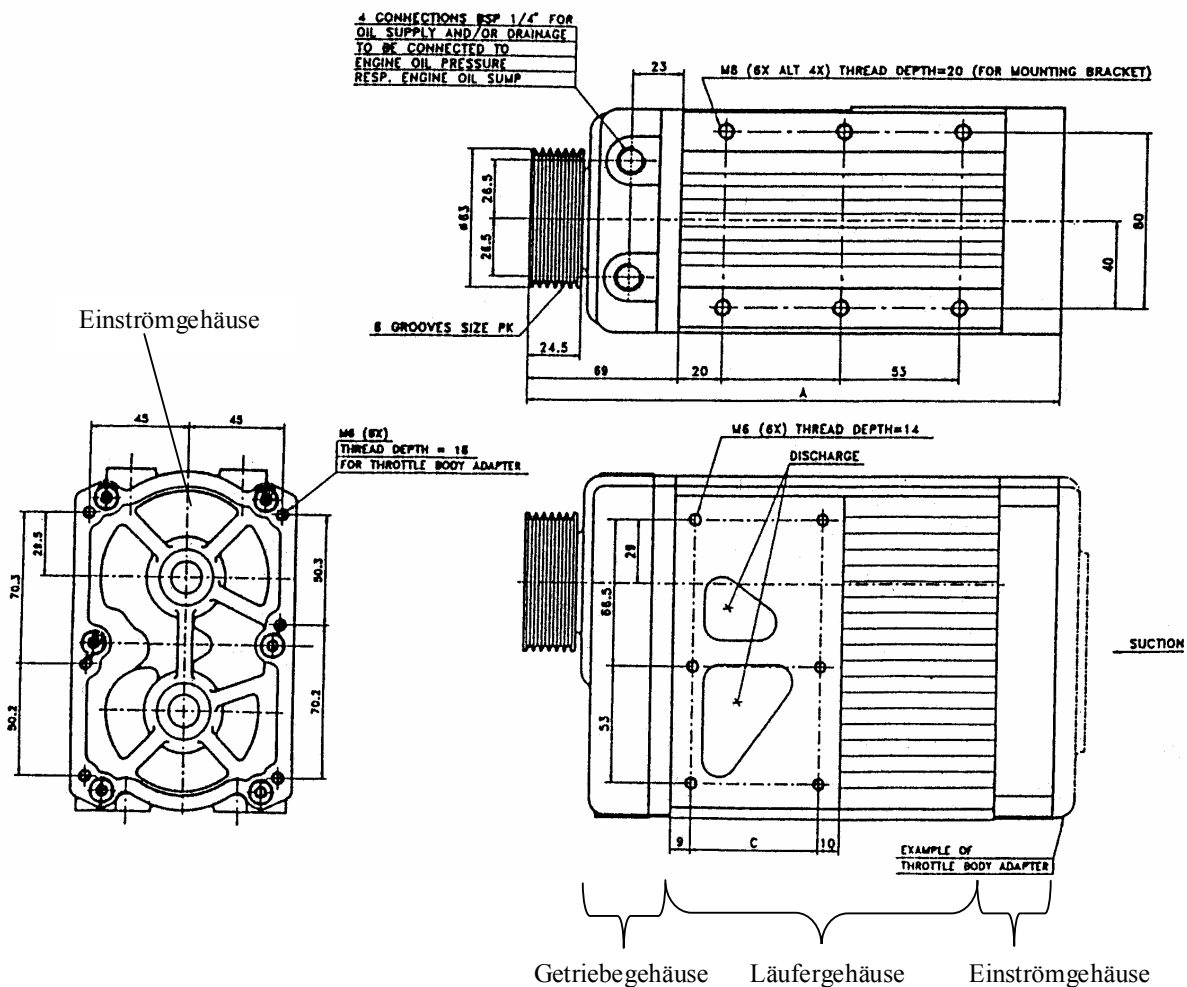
Verwendeter Basislader 'Opcon-Autorotor OA2089'
